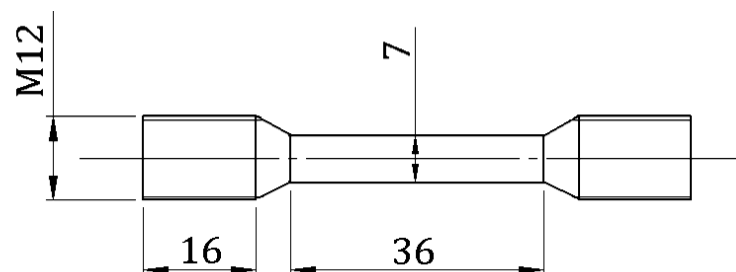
Eprouvette pour essais de traction, dimensions en mm.
